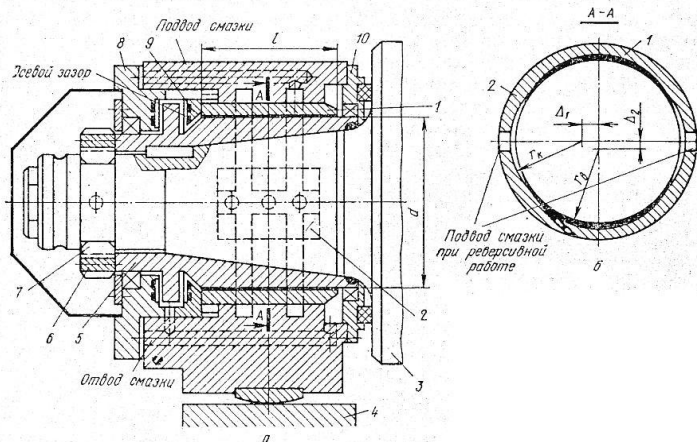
Конструктивные элементы подшипника жидкостного трения
